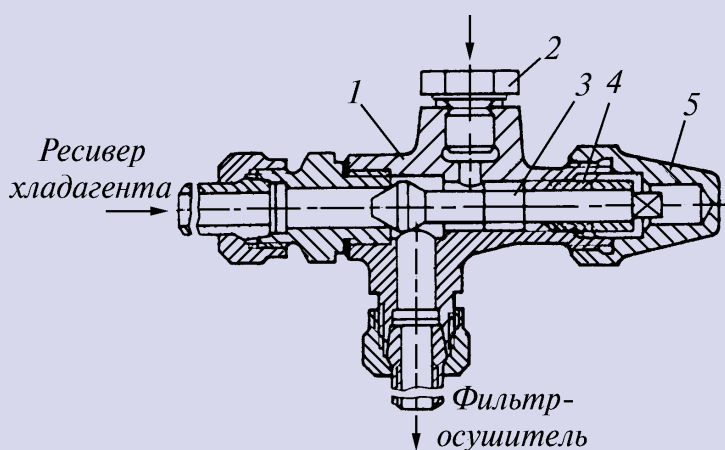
Угловой вентиль для заправки хладагентом: 1 — корпус; 2 — запорный болт; 3 — шпindel; 4 — сальник; 5 — защитный колпачок
